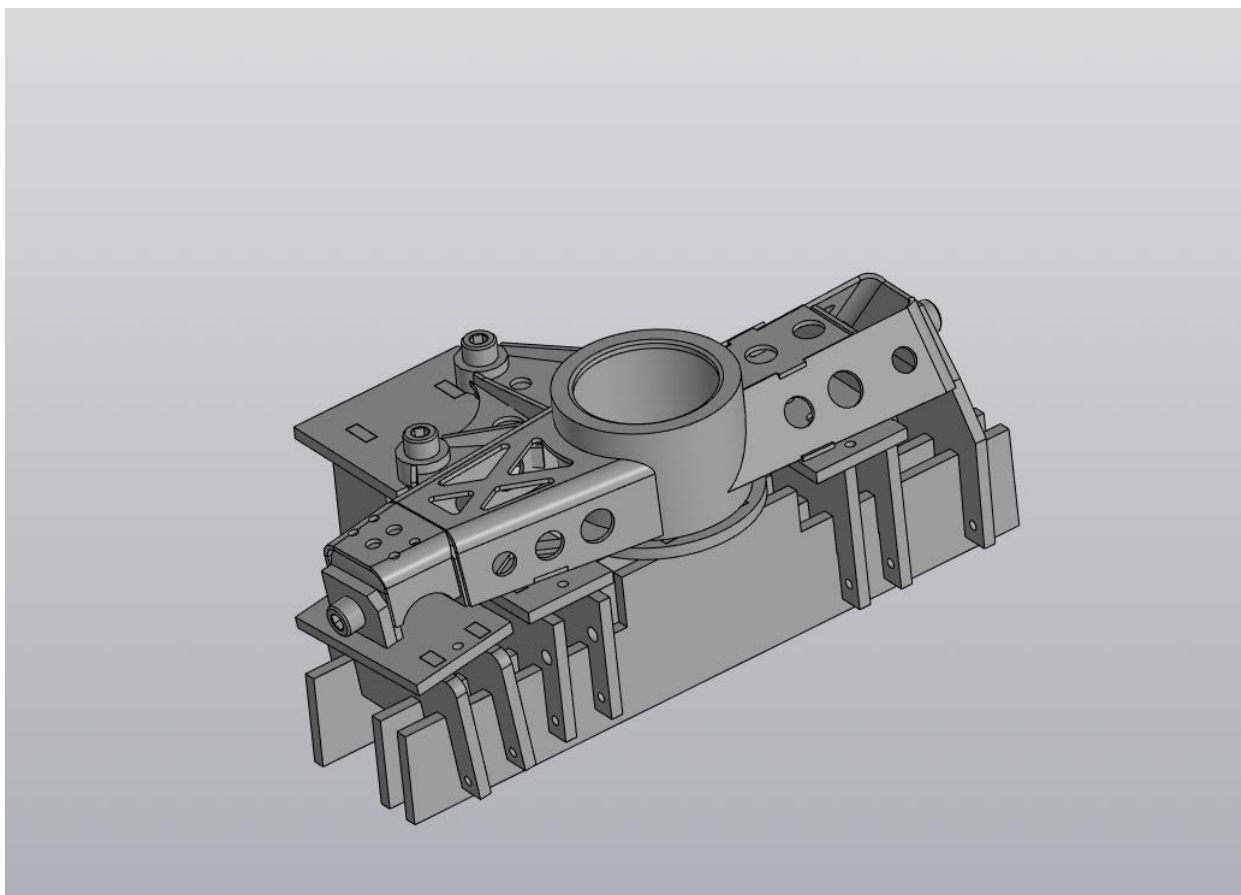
Стальной сварной поворотный кулак в стапеле
